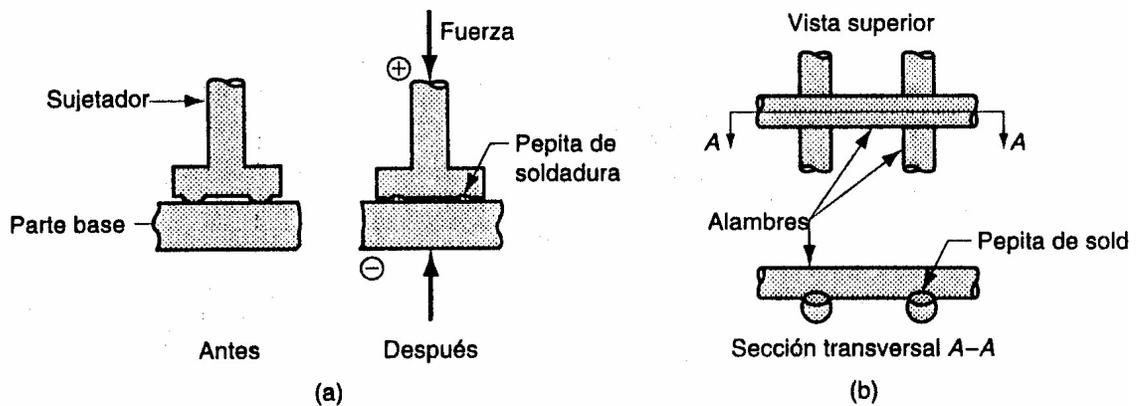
Dos variables de soldadura por proyección: (a) soldadura de un sujetador maquinado o formado sobre una parte de chapa de metal y (b) soldadura de alambre transversal
